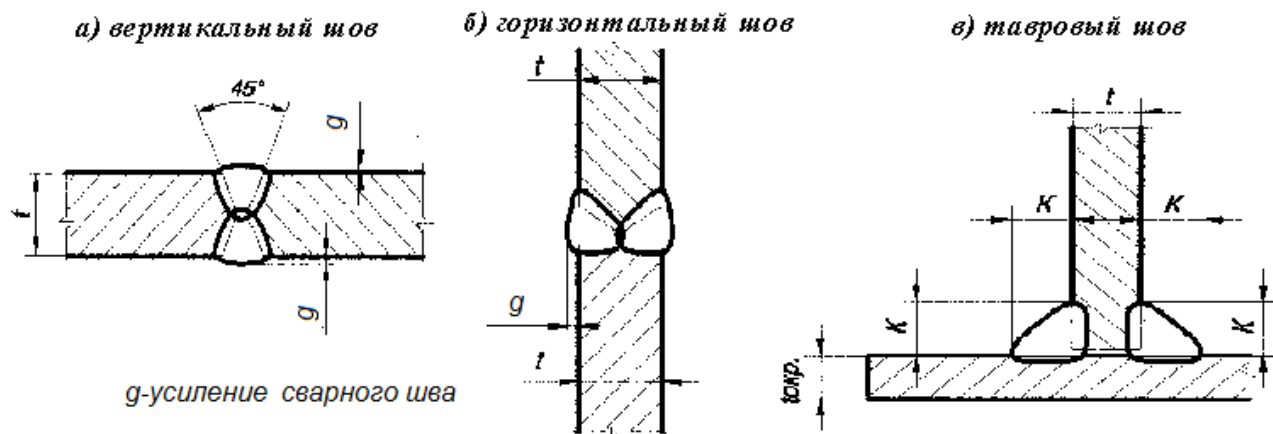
Сечения сварных швов ремонтной вставки
